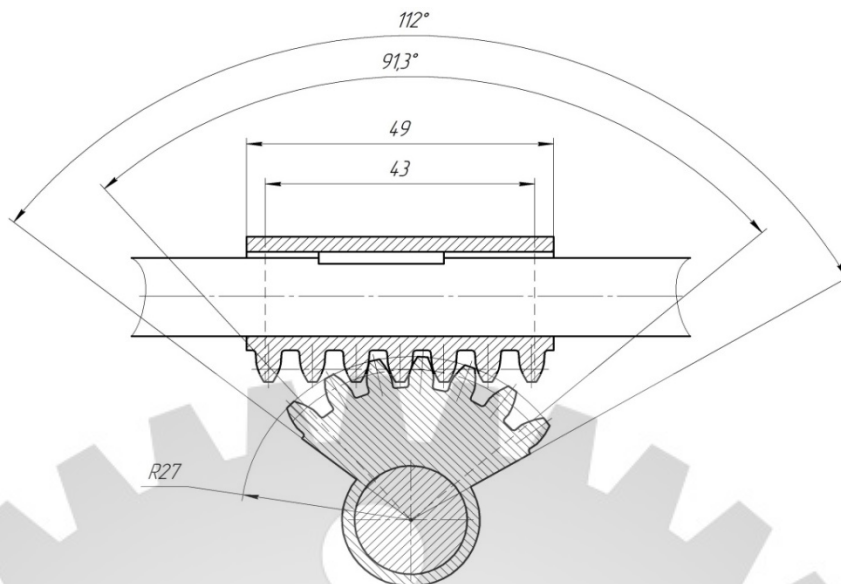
Механізм переключення блоків коробки швидкостей з двома зубчатыми колесами
